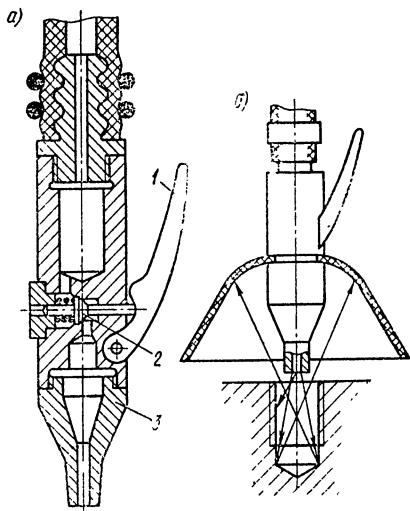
Наконечники для обдувки деталей сжатым воздухом
